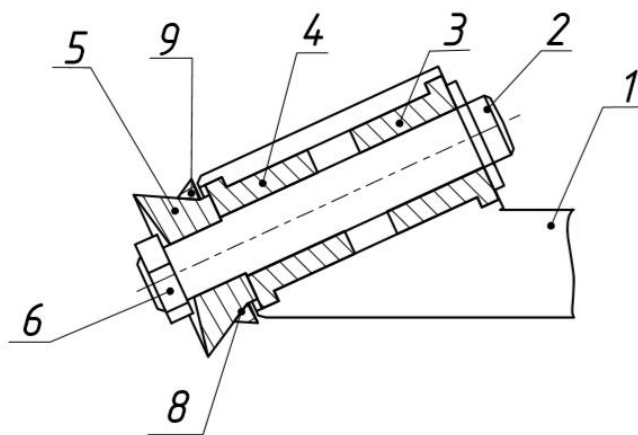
Схема ротаційного різця з графітовими підшипниками
